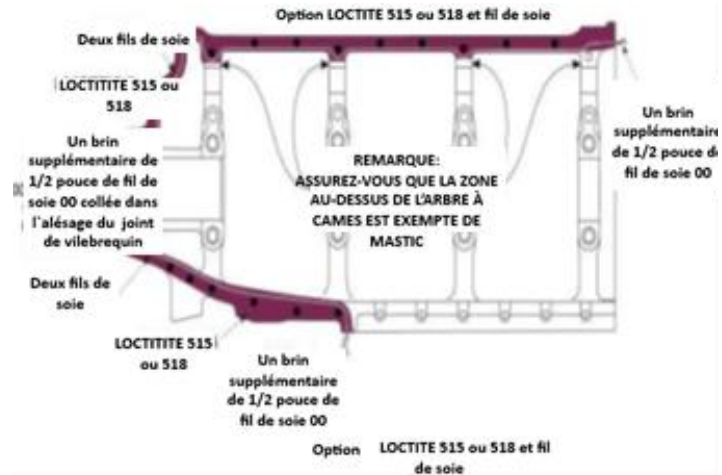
SI 1125E de Lycoming – Produits d'étanchéité alternatifs sur les surfaces de joint du carter moteur
